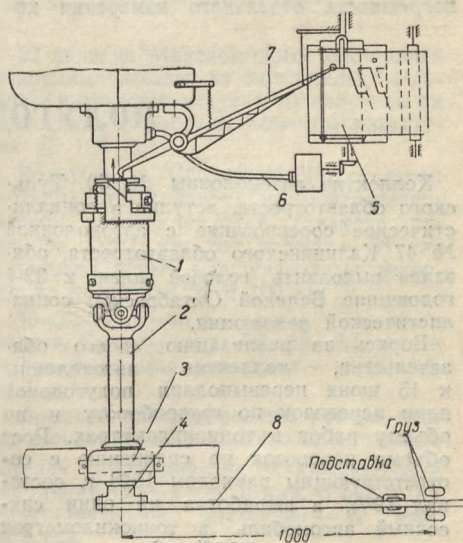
Схема установки прибора на автомобиле и приспособления для тарировки прибора.
